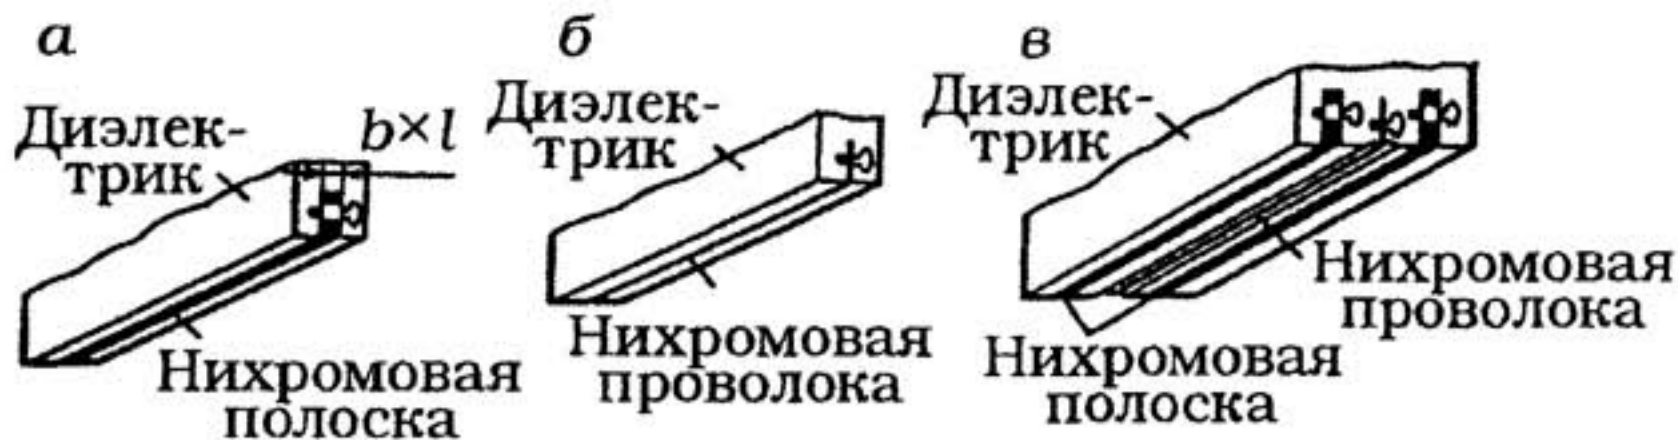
Нагревательный инструмент термоимпульсной сварки:
